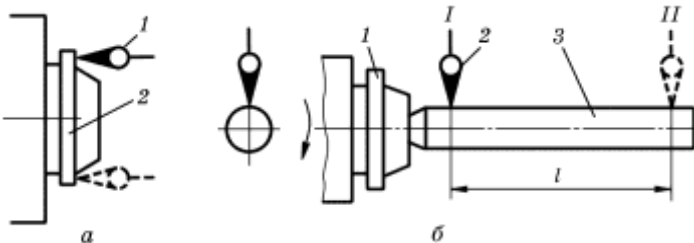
Схеми визначення торцевого биття опорної поверхні (а) і радіального биття внутрішньої центрувальної поверхні (б) шпинделя передньої бабки
